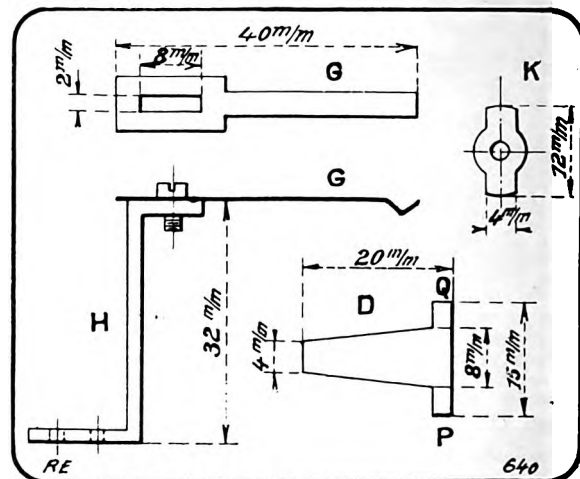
DONNÉES PRATIQUES POUR LE DÉCOUPAGE ET L'ASSEMBLAGE DES LAMES ET DU COLLECTEUR. — G, H, lames de contact et support ; K, pièce conductrice sur le côté du collecteur ; D, P, Q, lame du collecteur découpée en forme de trapèze.
